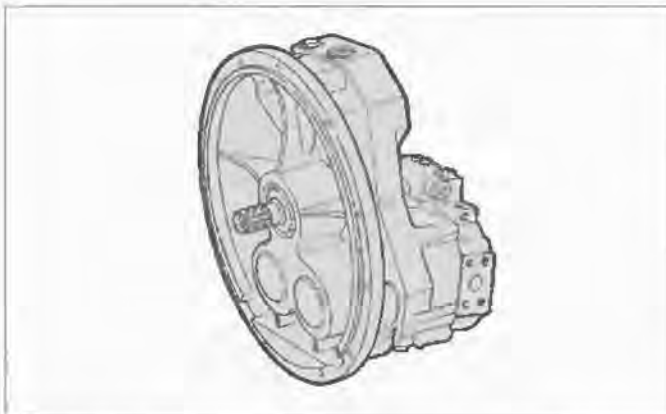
Регулируемый сдвоенный насос с общим приводным валом
